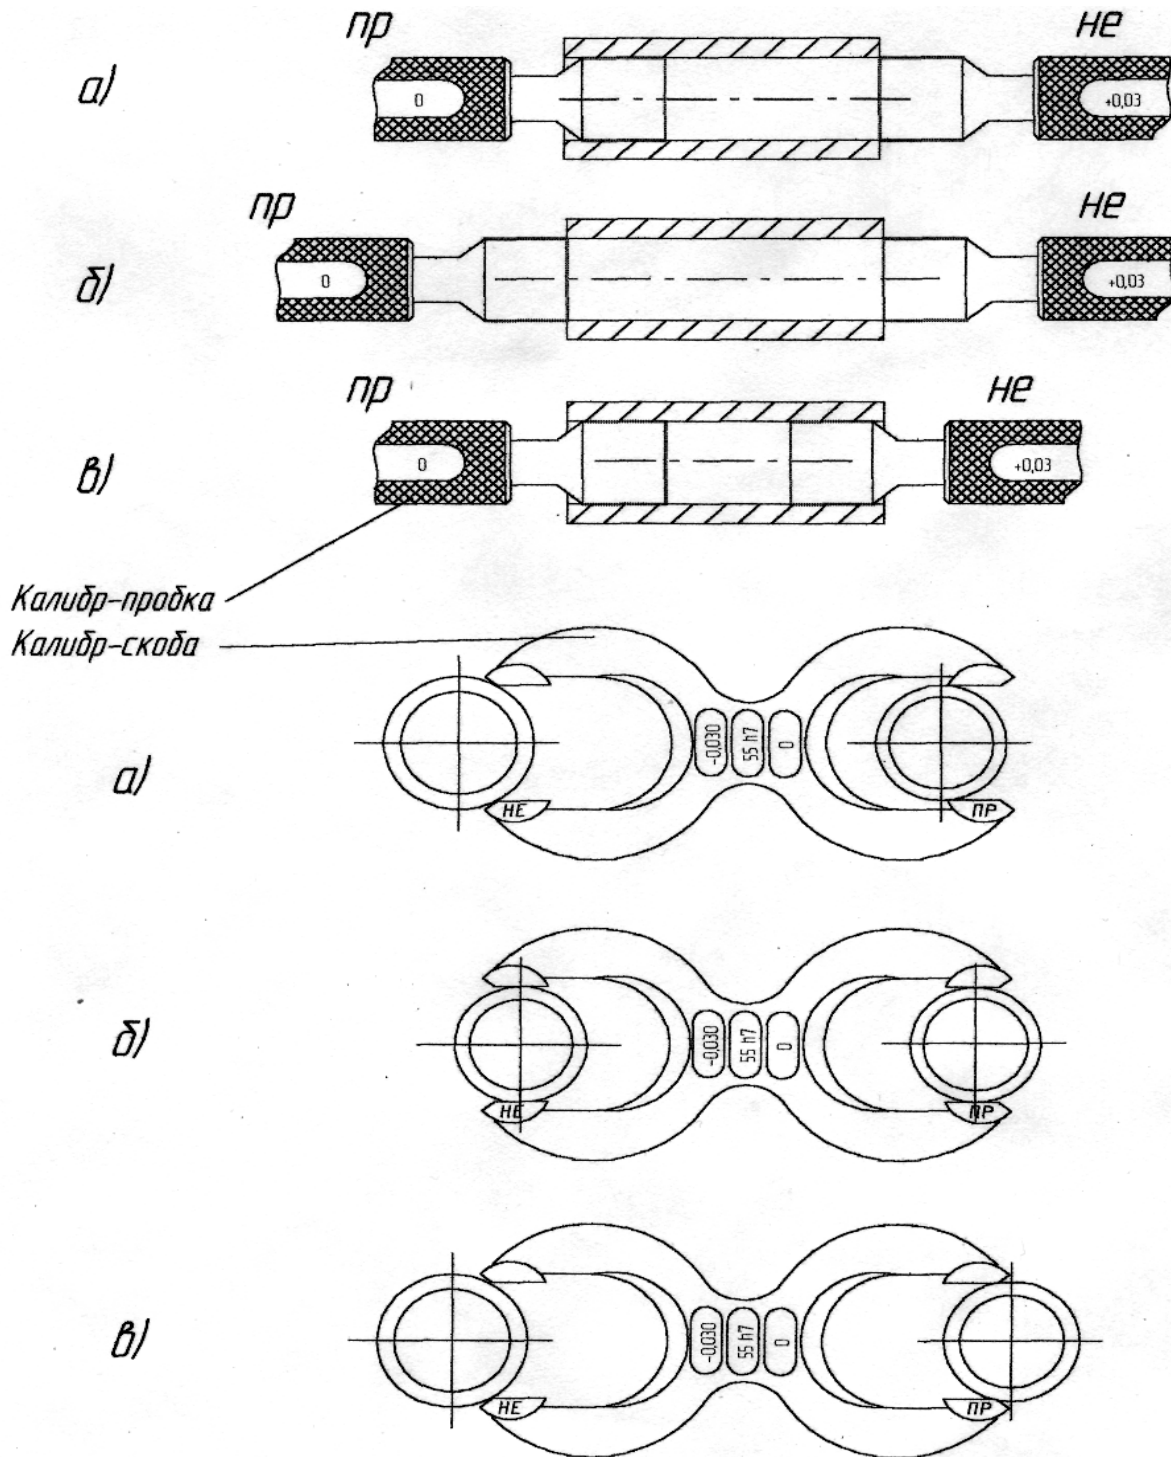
Контроль отверстия и вала придельными калибрами: а – детали годные, б – размер деталей меньше наименьшего допустимого, в – размер деталей больше допустимого наибольшего
